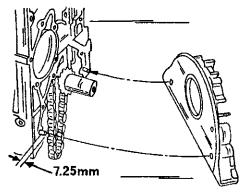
Установка переднего щитка подшилников. Обращать внимание на правильные выступы центрирующих штифтов. Поверхность, указанную правой стрелкой, покрыть уплотняющей массой.
